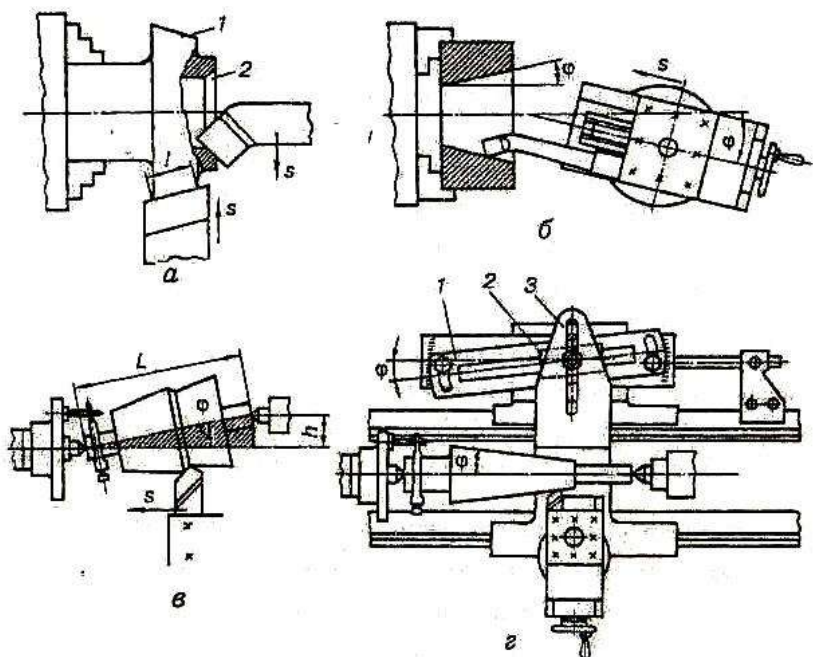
Обробка конічних поверхонь на токарному верстаті
